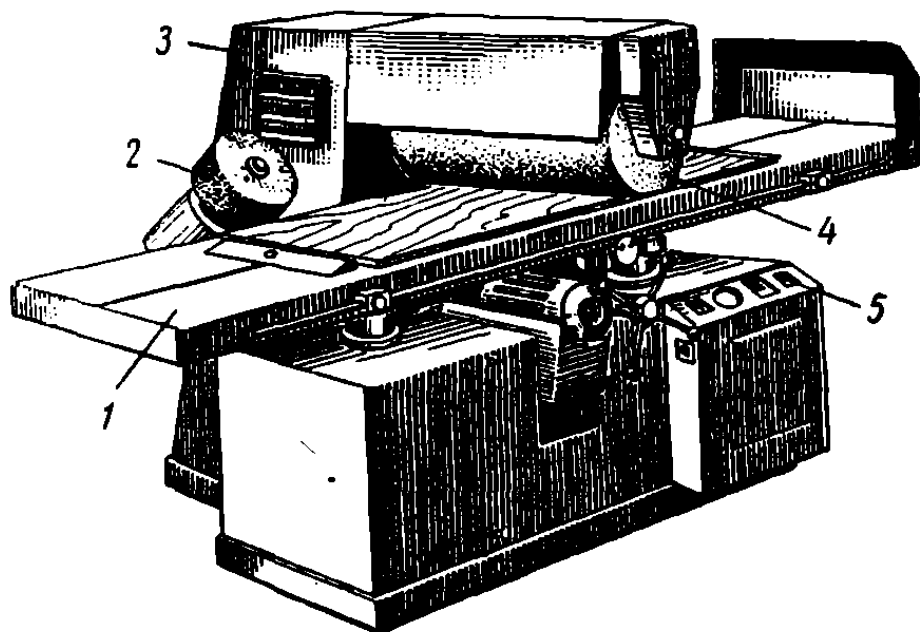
Полировальный автоматический вальцовый станок со съемным диском для полировки кромок: 1 — подвижный стол с эксцентриковым прижимом; 2 — барабан с набором эластичных дисков для полирования кромок; 3 — станина; 4 — барабан с набором фланцевых дисков для полирования пласти; 5 — пульт управления
